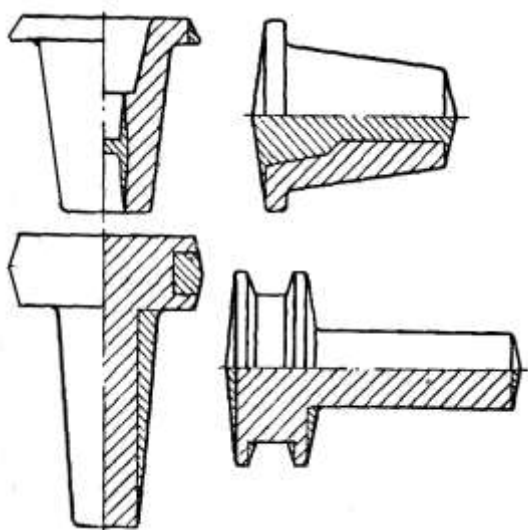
Вплив поверхні роз'єму штампу на форму поковок
